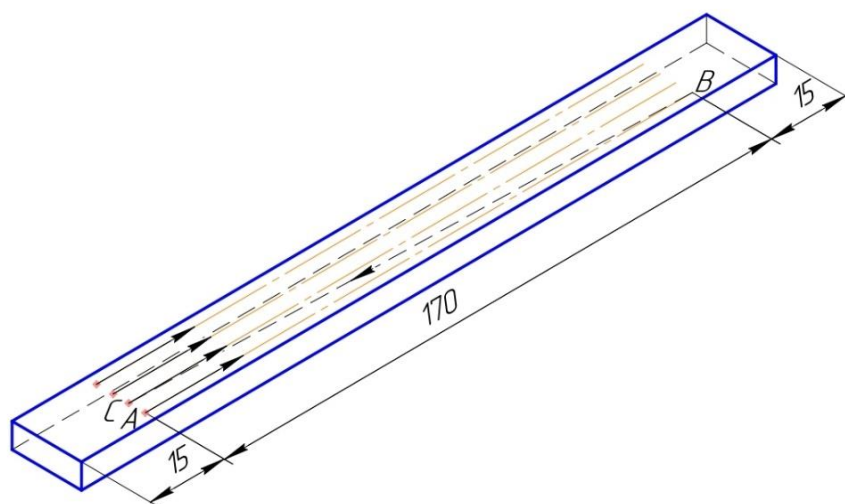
Схема движения лазерного пятна сканирования по поверхности образца
